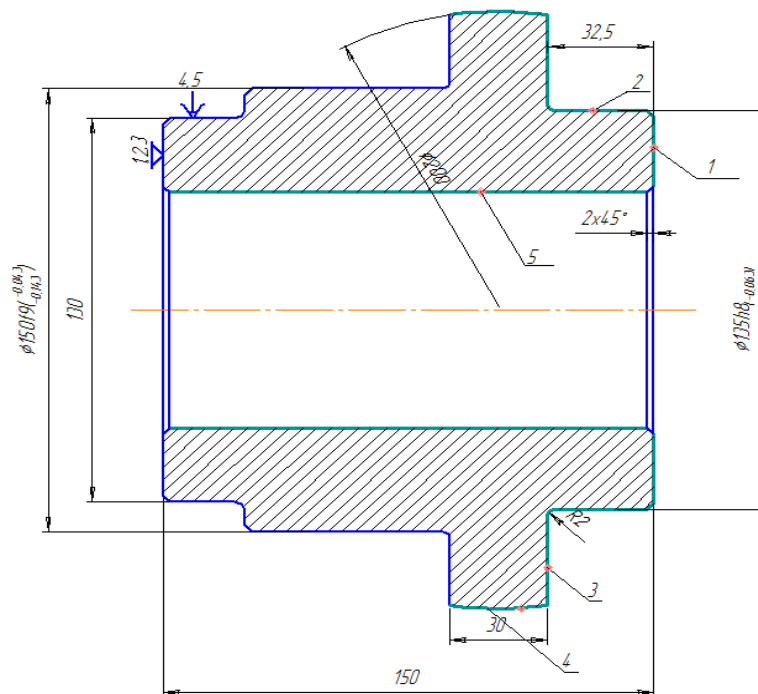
Схема базування деталі на операції 045 Токарна з ЧПК
